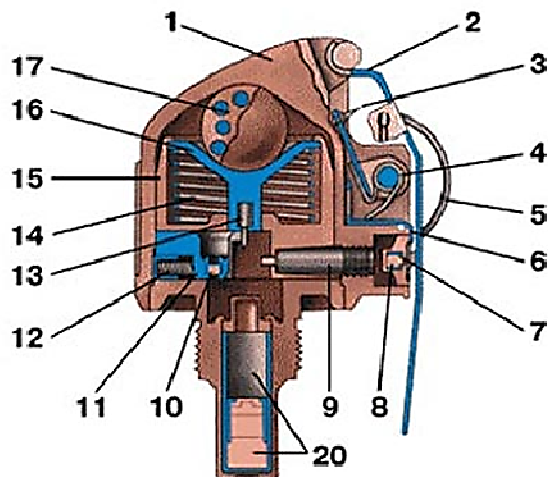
Устройство запала УДЗ: 1 – корпус; накольно-предохранительный механизм: 2 – спусковой рычаг; 3 – ударник с жалом; 4 – боевая пружина; 5 – кольцо с чекой; 6 – планка; 7 – заглушка; 8 – капсюль-воспламенитель; механизм дальнего взведения: 9 – пороховые предохранители; 10 – капсюль-воспламенитель; 11 – движок; 12 – пружина; датчик цели: 13 – жало; 14 – пружина; 15 – гильза; 16 – втулка; 17 – груз; механизм самоликвидатора: 18 – замедлитель; 19 – капсюль-детонатор; детонационный узел: 20 – капсюль-детонатор
